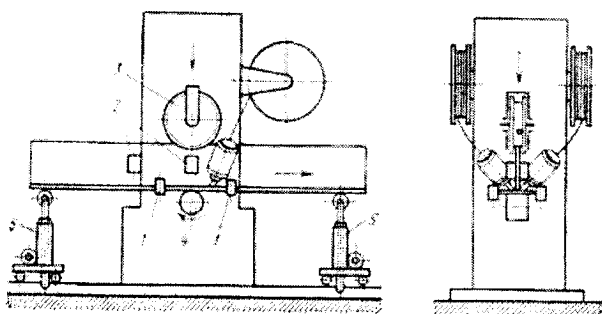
Схема станка СТС для складання і зварювання балок
